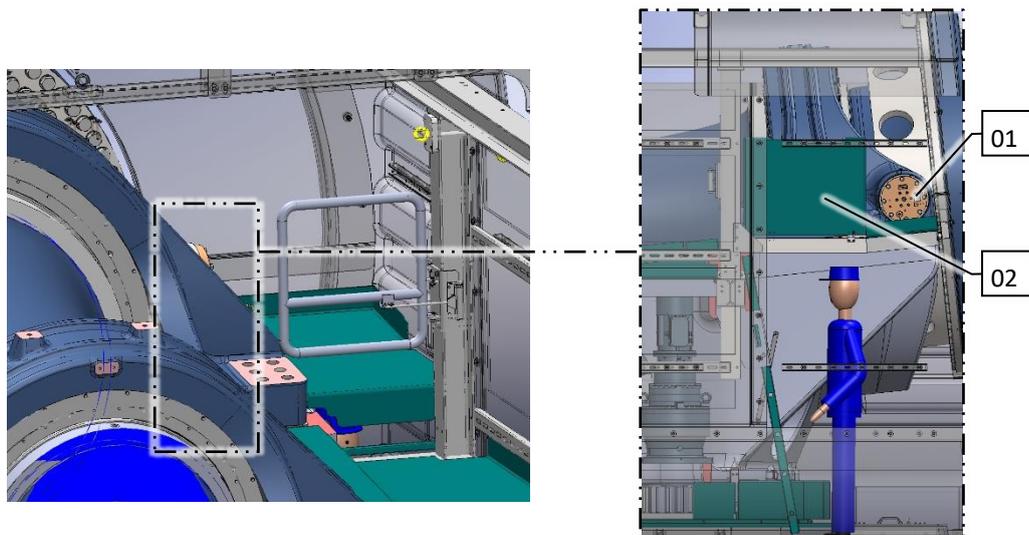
Rotorlock mit Schlüsseltransfersystem
